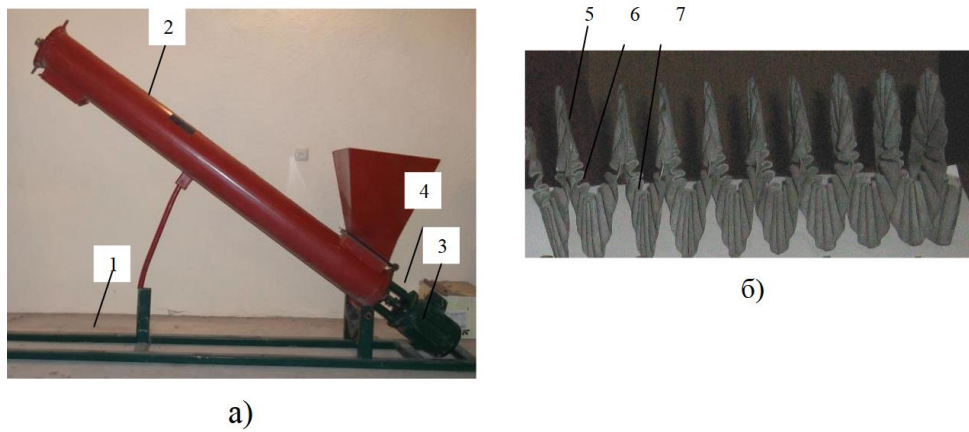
Вузол підготовки суміші до екструдювання: а) – загальний вигляд, 1 – рама; 2 – кожух; 3 – електродвигун; 4 – муфта; б) – загальний вигляд робочого органу, 5 – гофрований робочий орган; 6 і 7 – впадини і виступи гофр.
